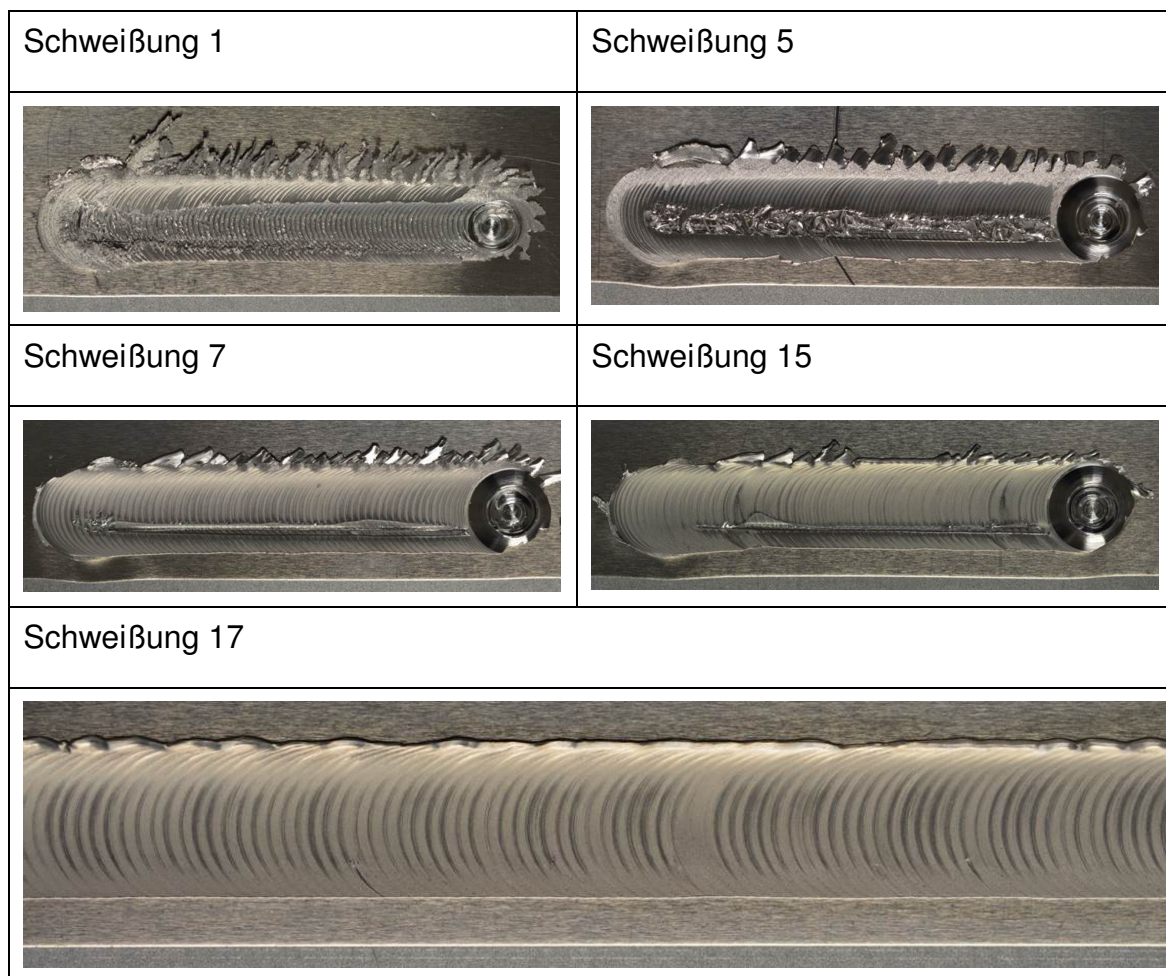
Ausgewählte Schweißnahtoberflächen CR660Y980T und EN AW 7075 T6
